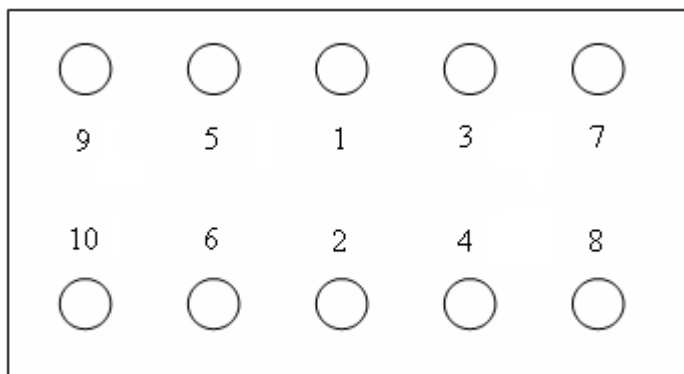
Схема затяжки гаек коренных подшипников двигателя Д-50.
